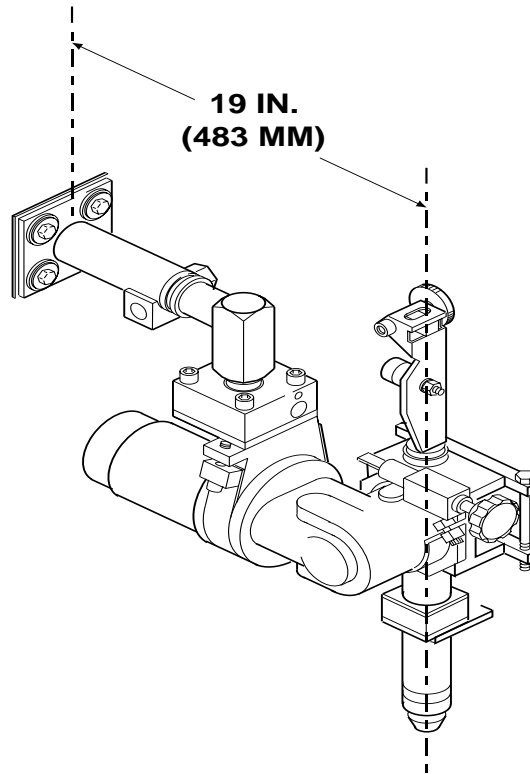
ORIFICIOS DE MONTAJE DEL CABEZAL DE SOLDADURA.
